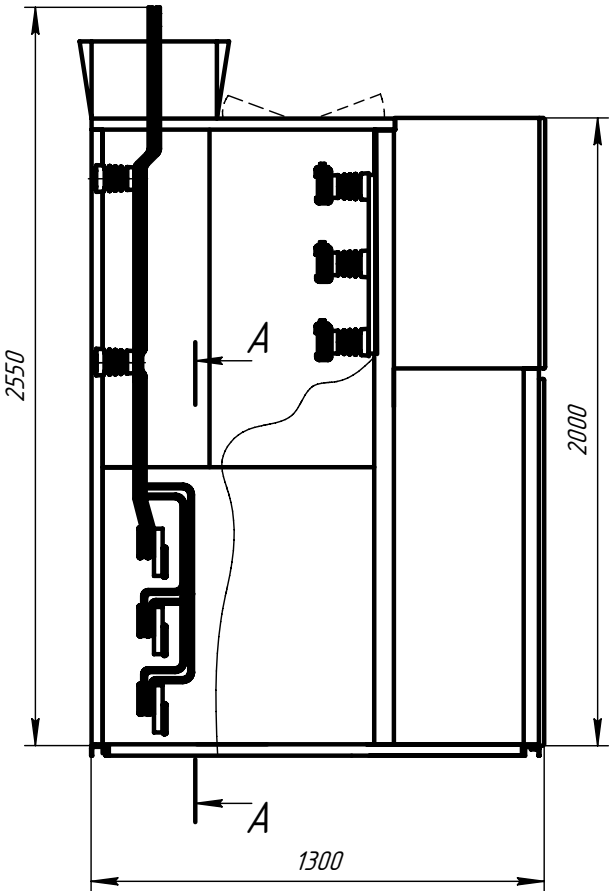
Габаритные, установочные, присоединительные размеры шкафов.
